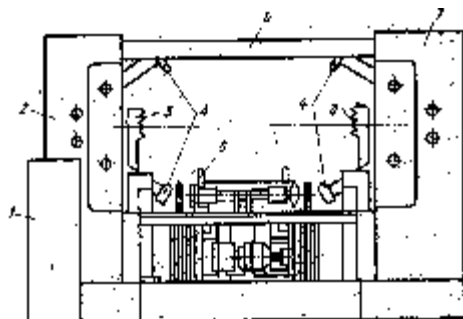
Схема центровочно - загрузочного устройства ЦЗУ 17-10 : 1-пневмоцилиндр, 2, 7 - левая и правая стойки, 3 - механизм переноса чурака, 4- механизм вертикальной центровки, 5 - поперечина, 6 - механизм горизонтальной центровки.
